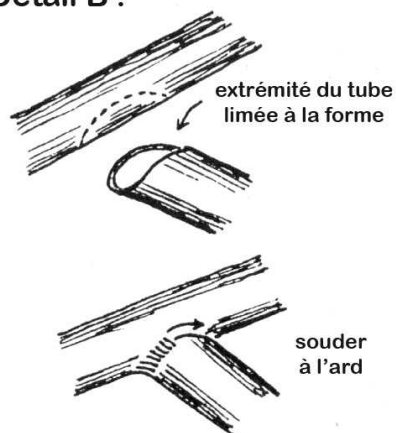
Figure B : adapter le tube à la lime demi-ronde et souder à l'arc.
